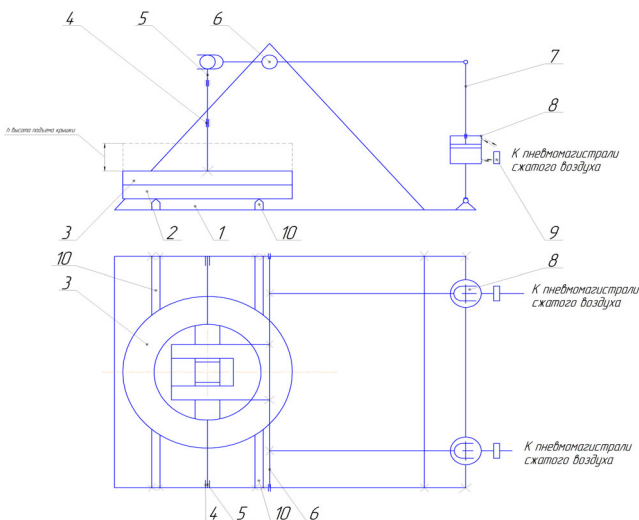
Принципиальная кинематическая схема приспособления для открывания и закрывания закалочного устройства
